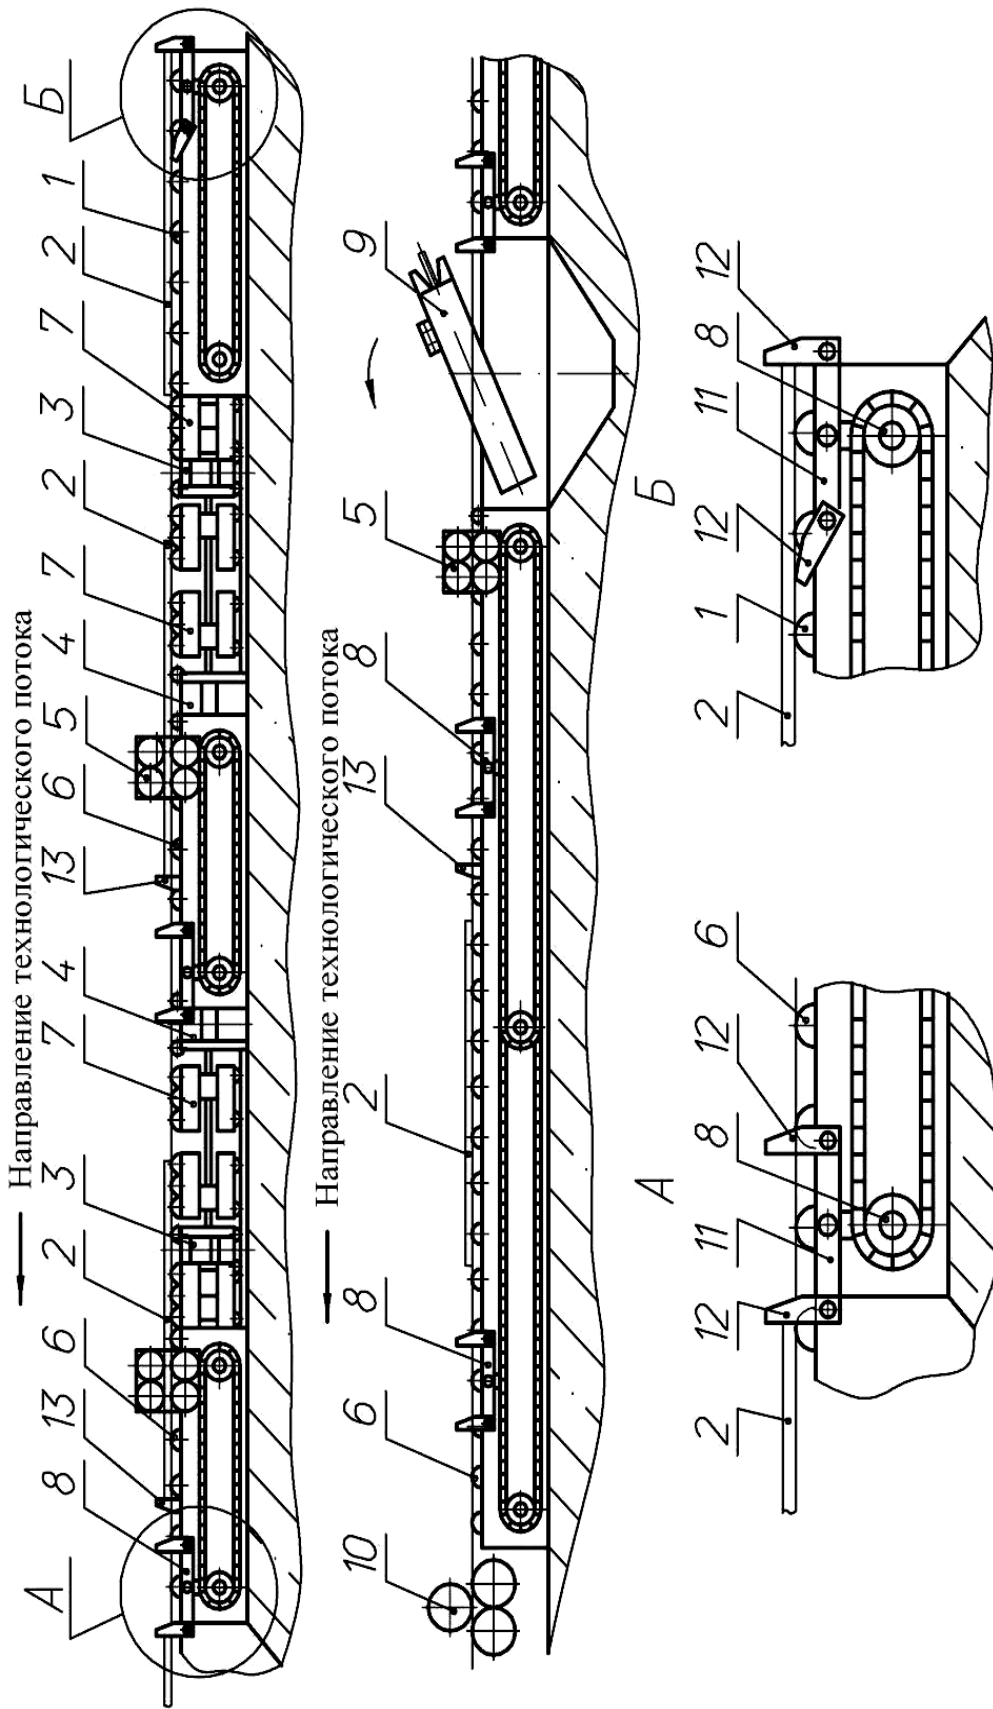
Схема транспортной системы универсальной линии сборки и сварки листовых полотнощ:
